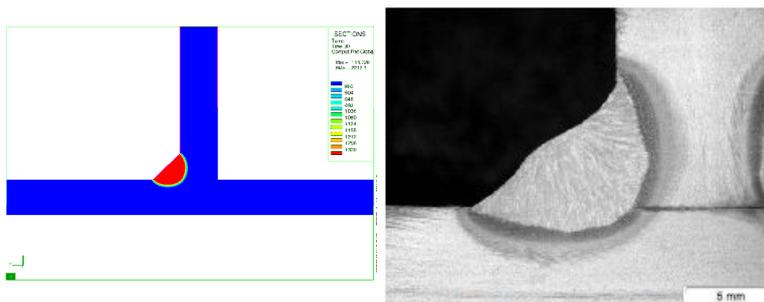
Simulation SYSWELD du chargement thermique et vue du cordon de soudure
